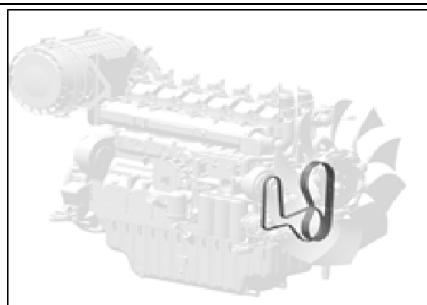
И- Проверка натяжки приводного ремня
